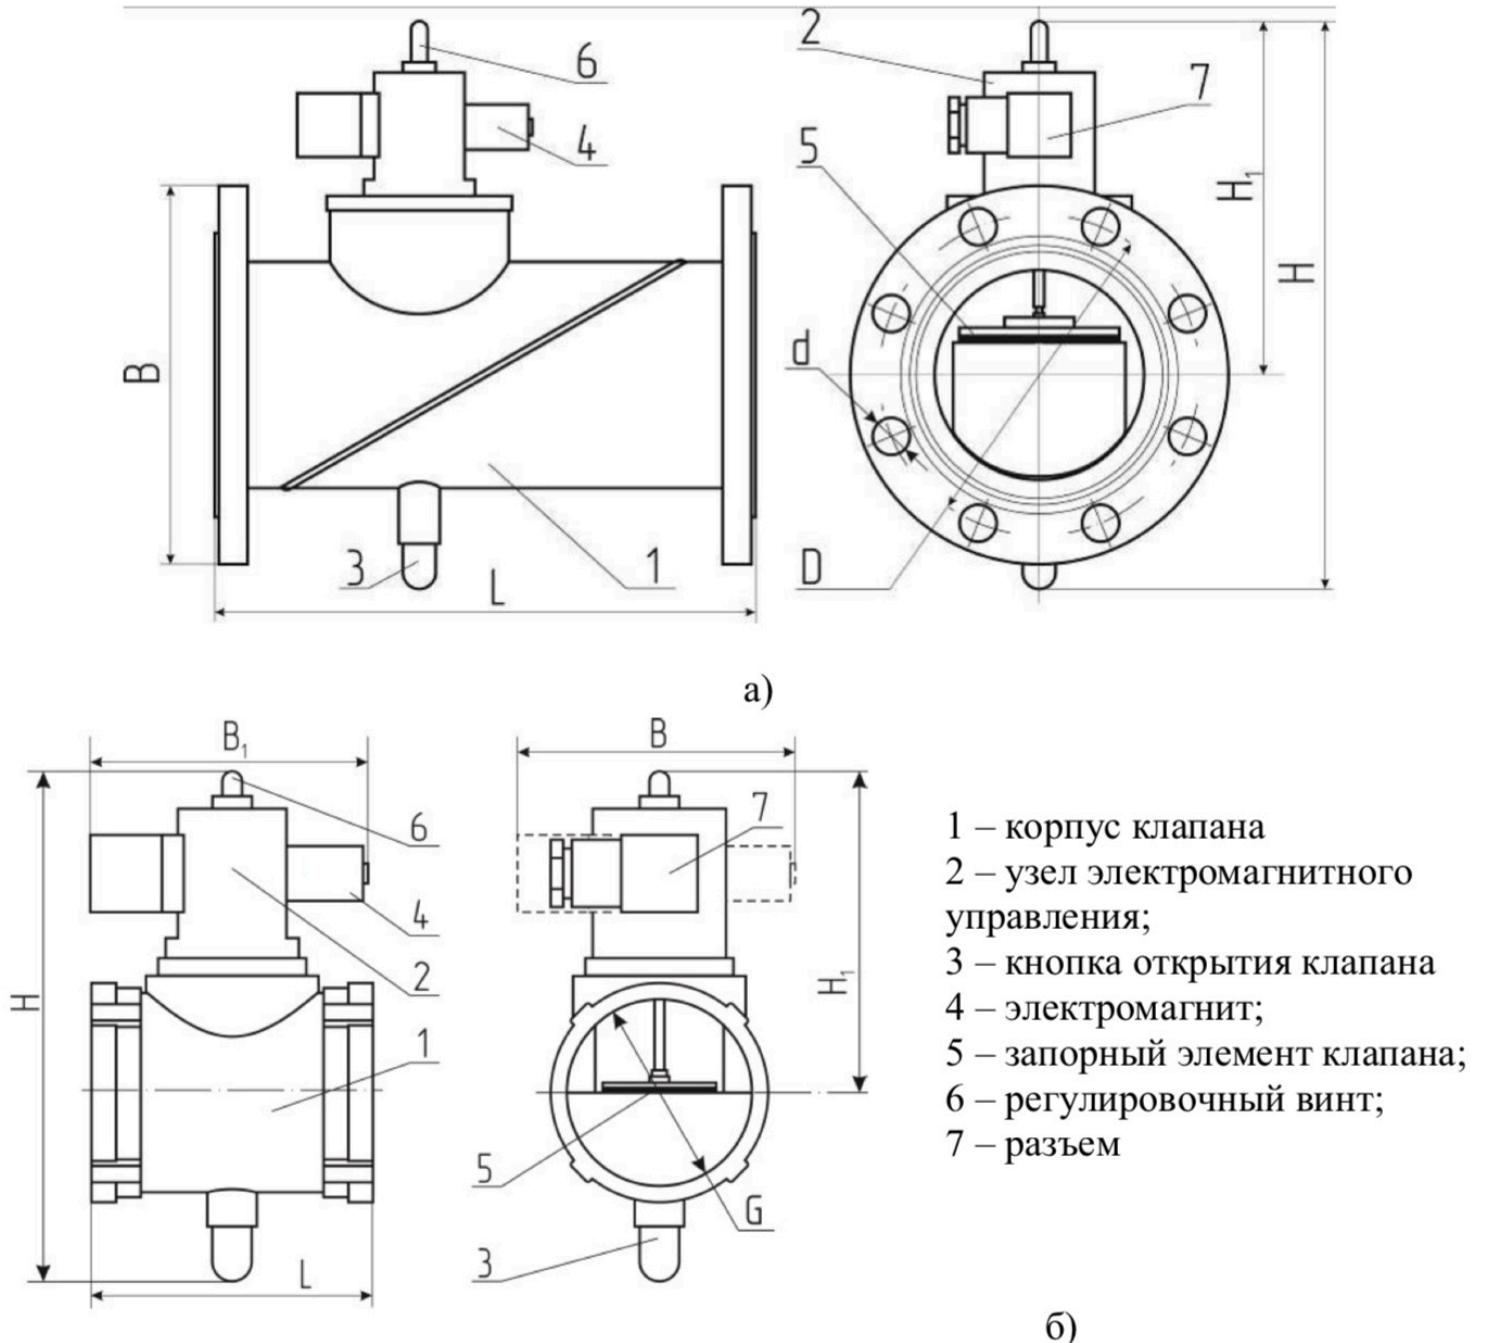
Внешний вид клапана: а) фланцевый; б) муфтовый
